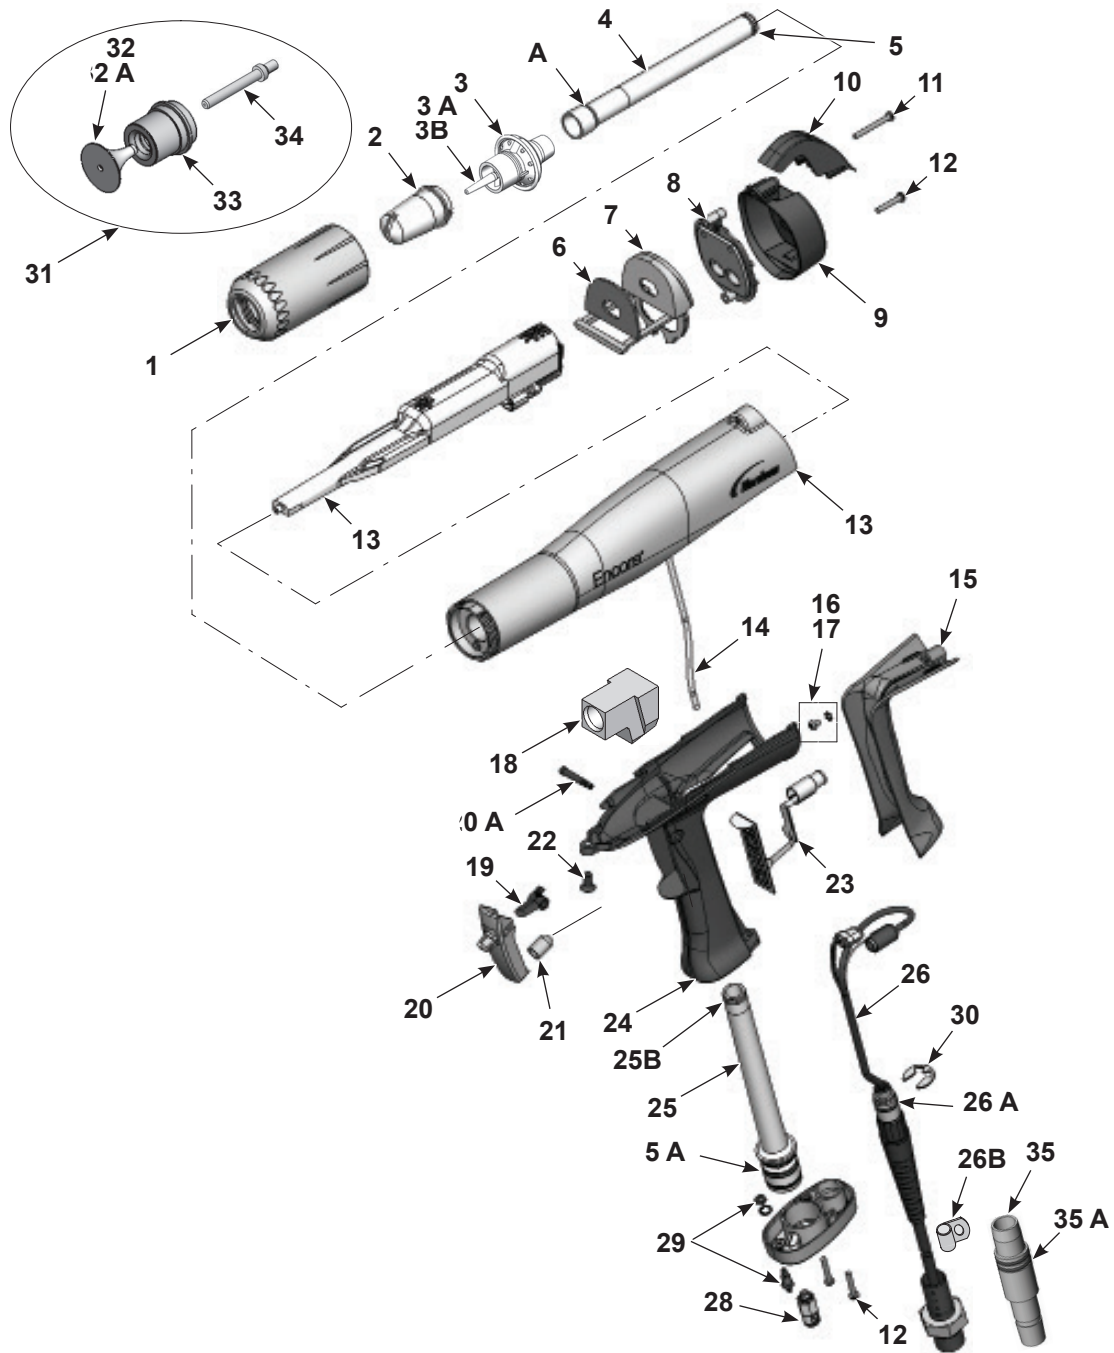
Vue éclatée du pistolet de pulvérisation manuel Encore LT et de ses accessoires
